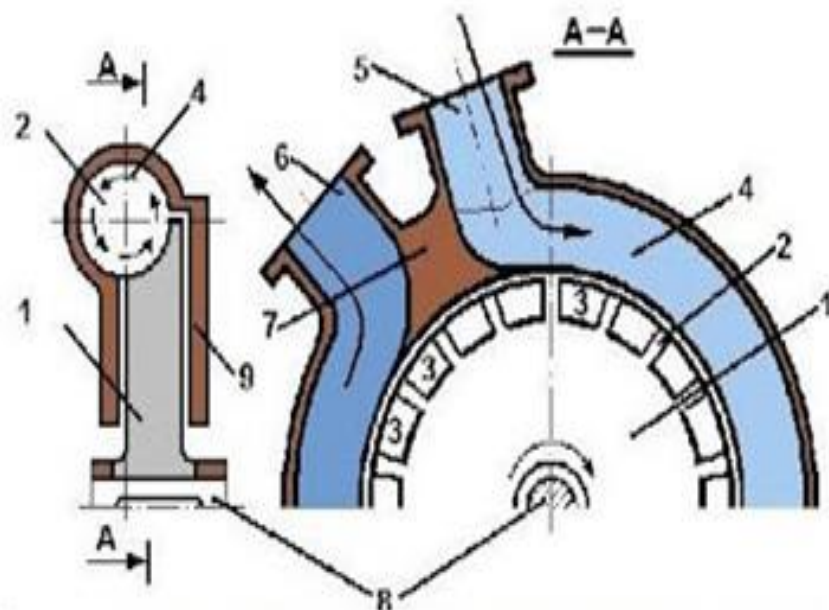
Вихревые насосы: 1 – рабочее колесо; 2 – лопатки; 3 – межлопастные каналы; 4 – кольцевой отвод; 5, 6 – всасывающий и нагнетательный клапаны; 7 – разделитель потоков; 8 – вал; 9 – корпус
